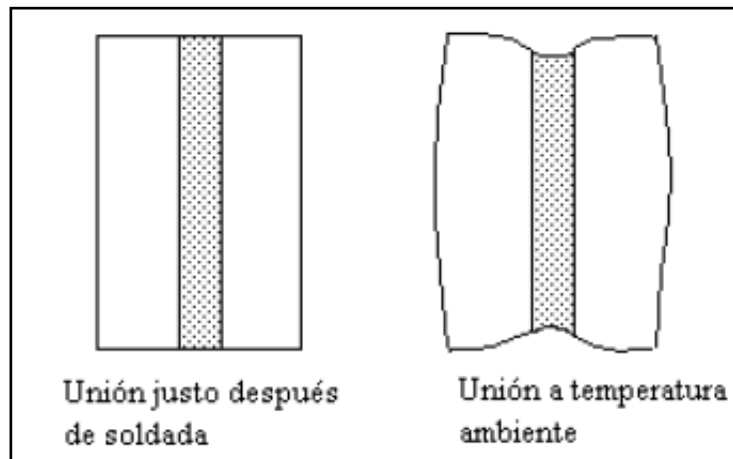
Geometrías de las piezas soldadas. (The Procedure Handbook of Arc Welding, 1995.)
